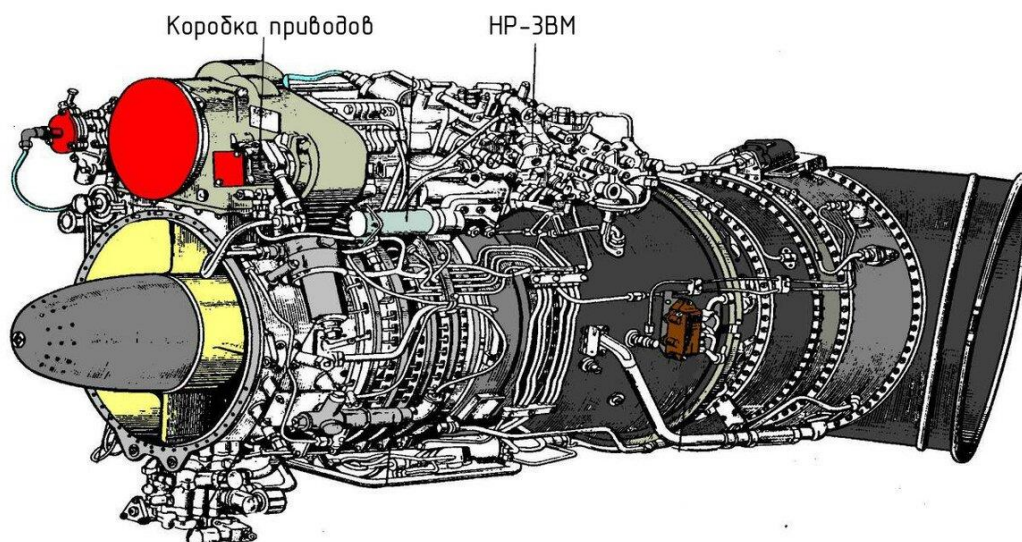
Общій вид двигателя ТВ3-117 конструкции С.П. Изотова.
